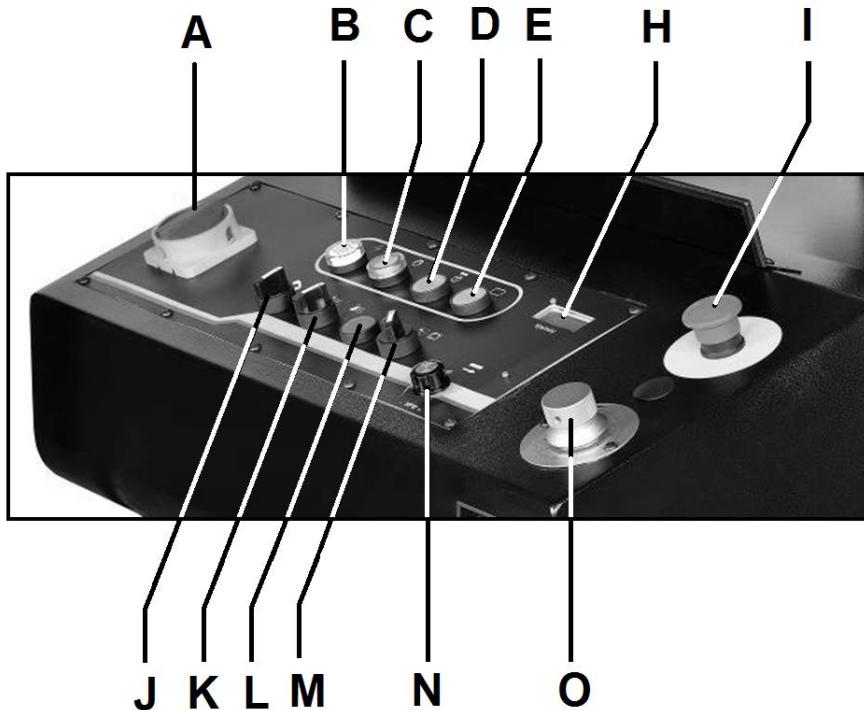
Bezeichnungen der Bedienelemente der Maschine
